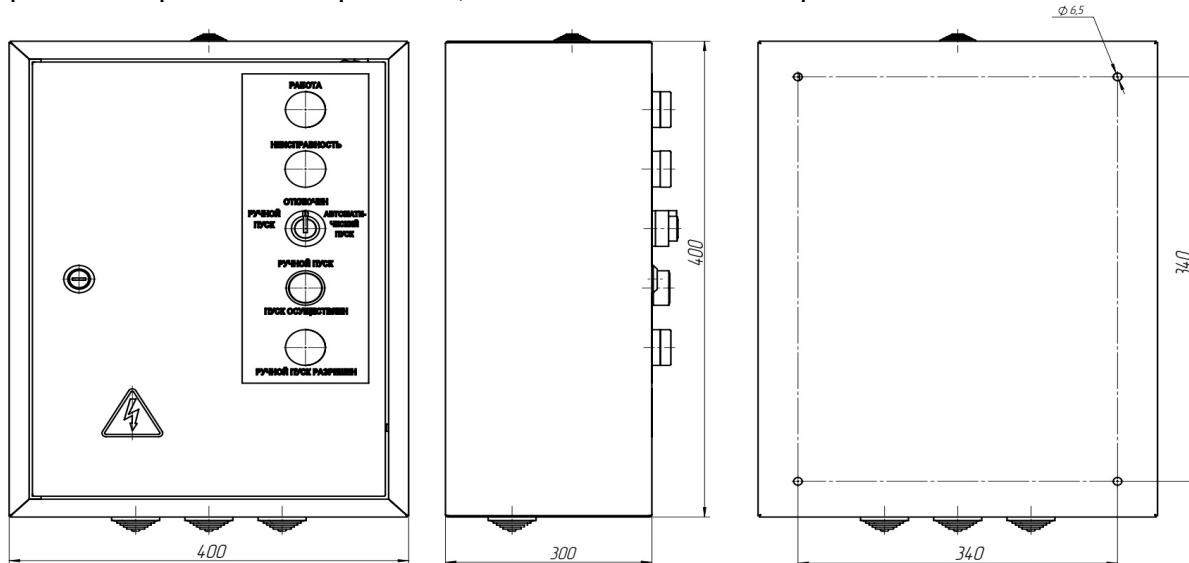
Габаритные и установочные размеры ШУП-XX исп.1К.
